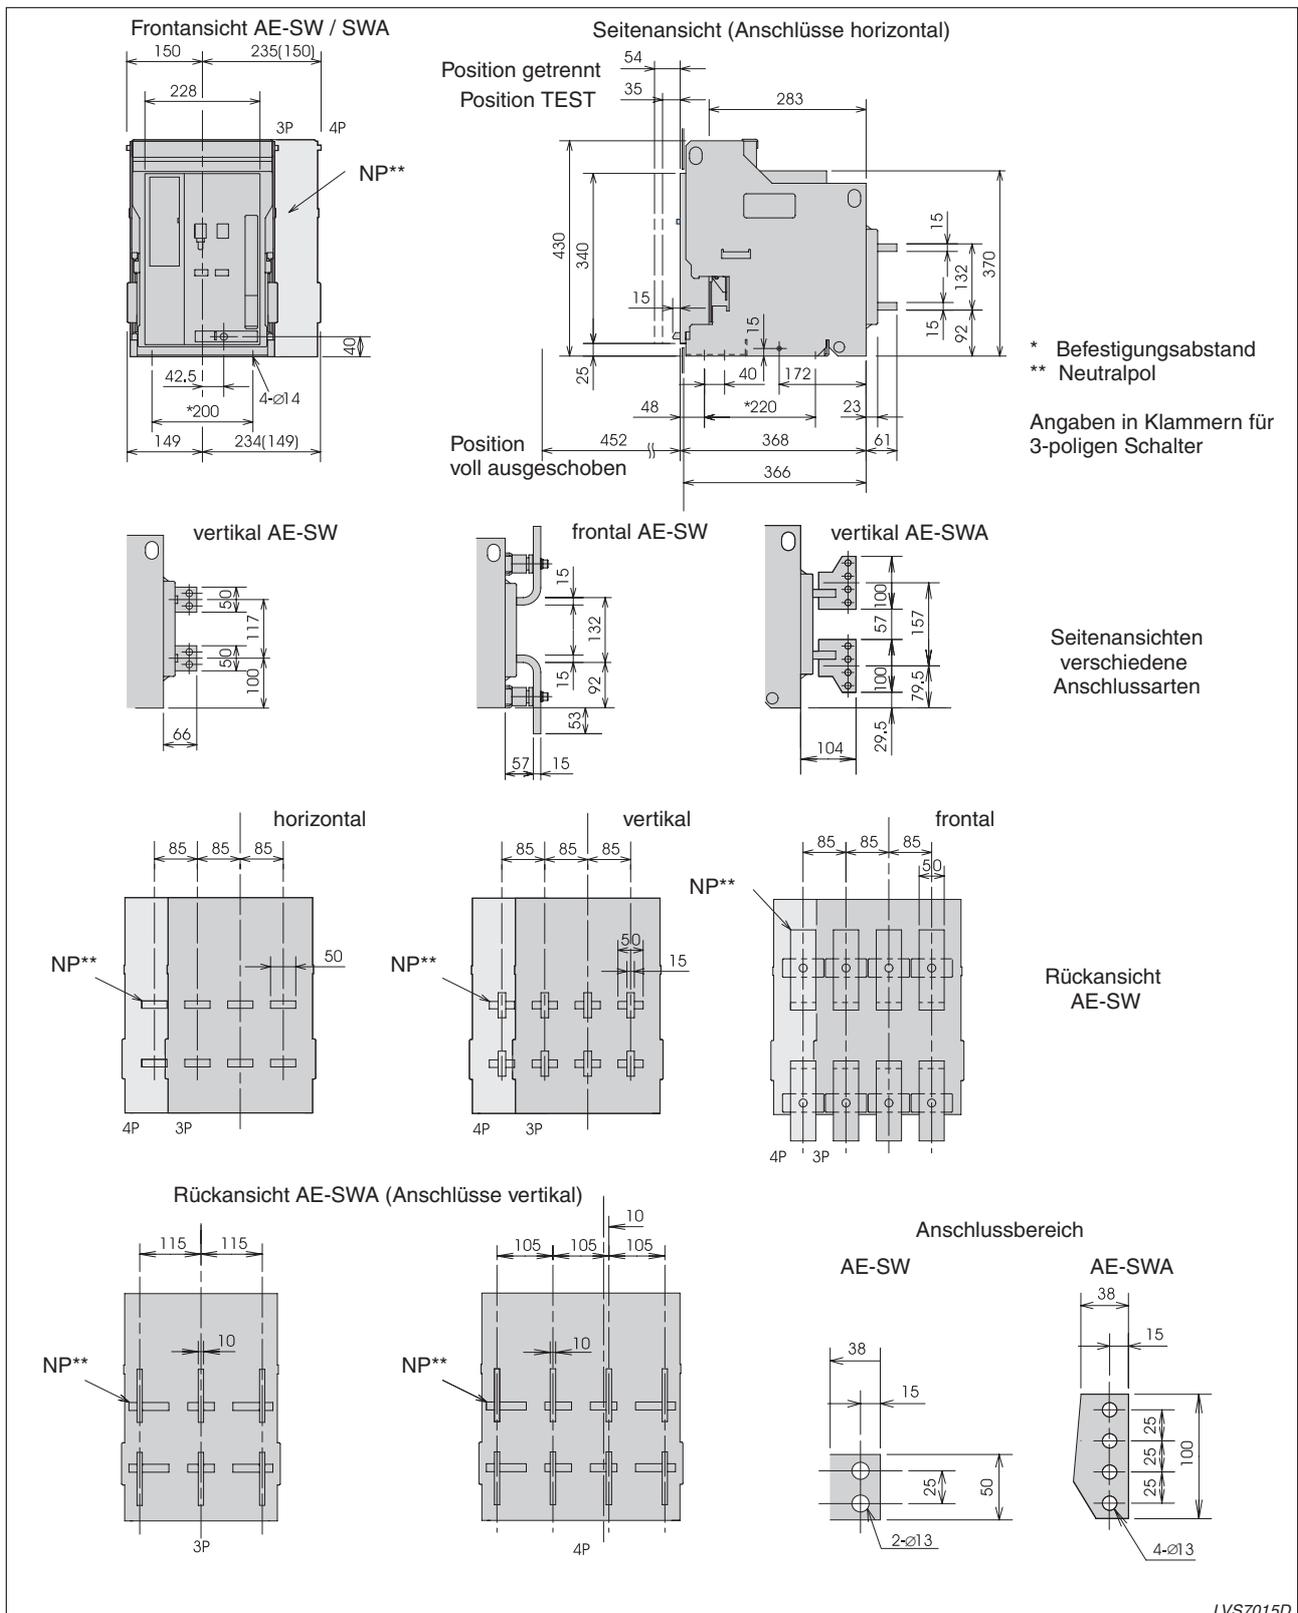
Abmessungen (in mm) der Einschubtyp-Schalter
